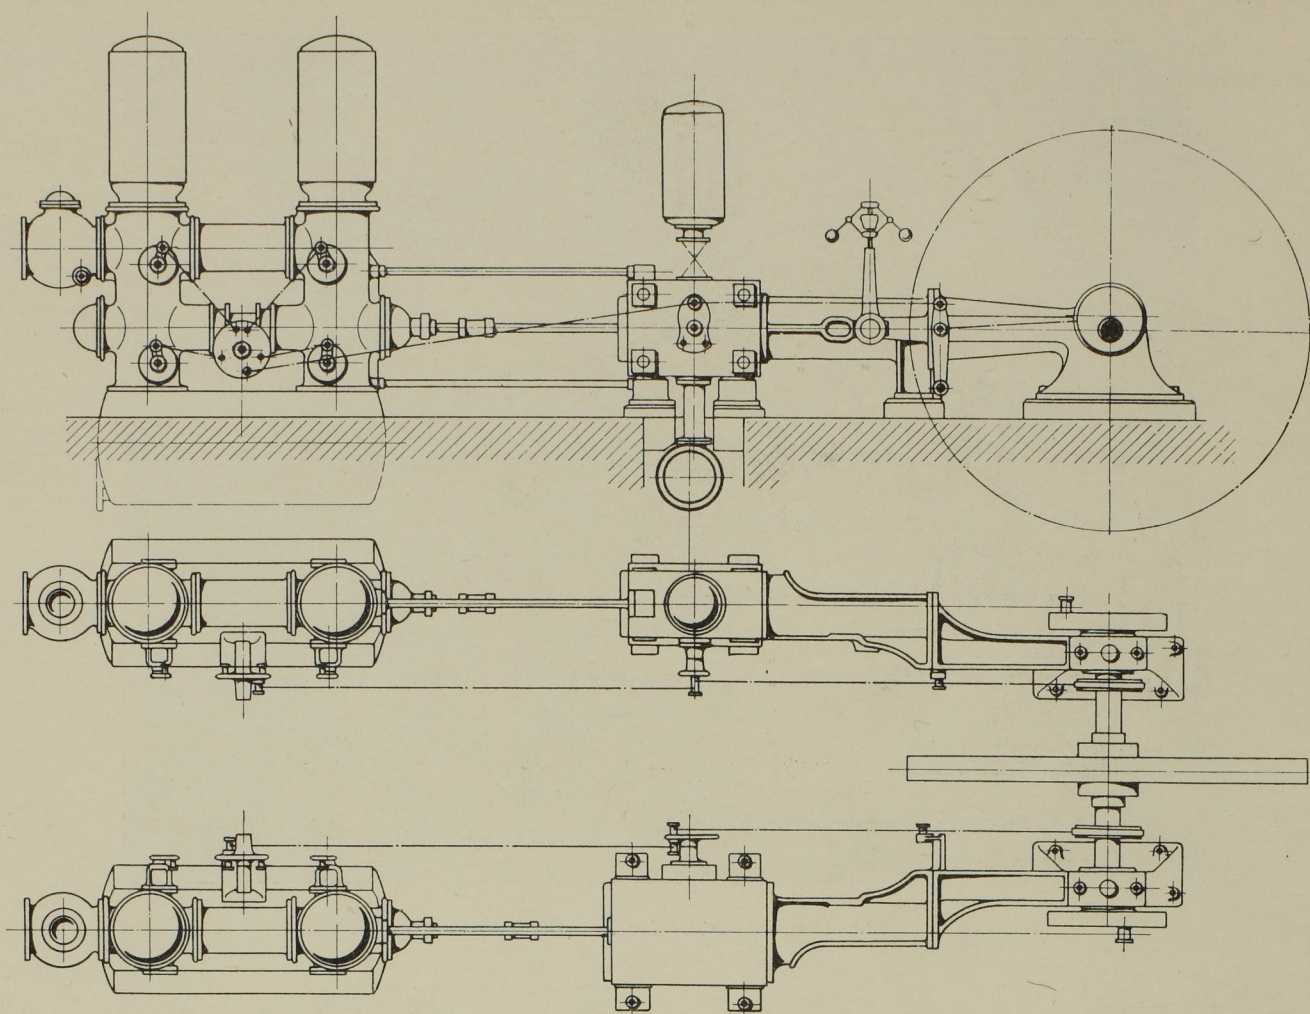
Seitenansicht und Grundriss. Massst. 1:72.
